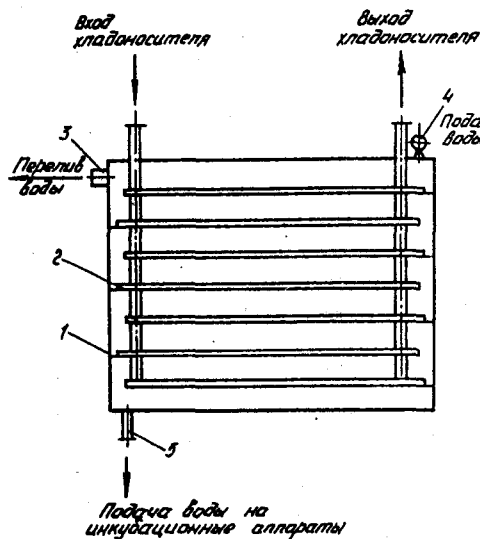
Теплообменник: 1 - корпус; 2 - батарея для охлаждения (подогрева); 3 - переливная труба; 4 - коллектор; 5 - патрубок для слива воды
